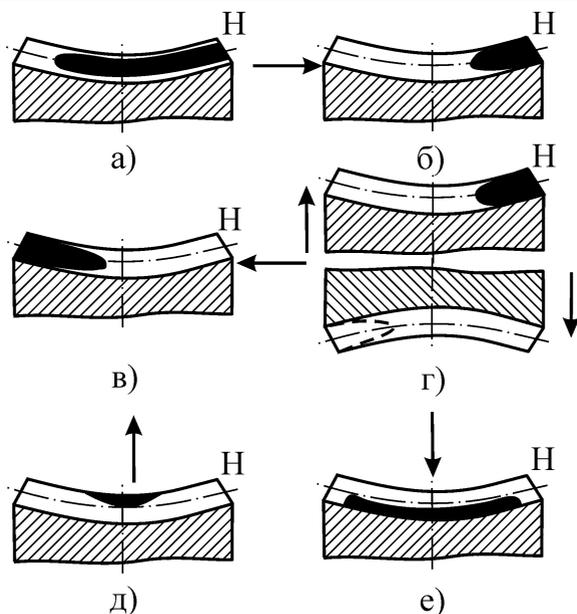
Проверка правильности установки червячного колеса относительно червяка с помощью отпечатка краски на зубьях
